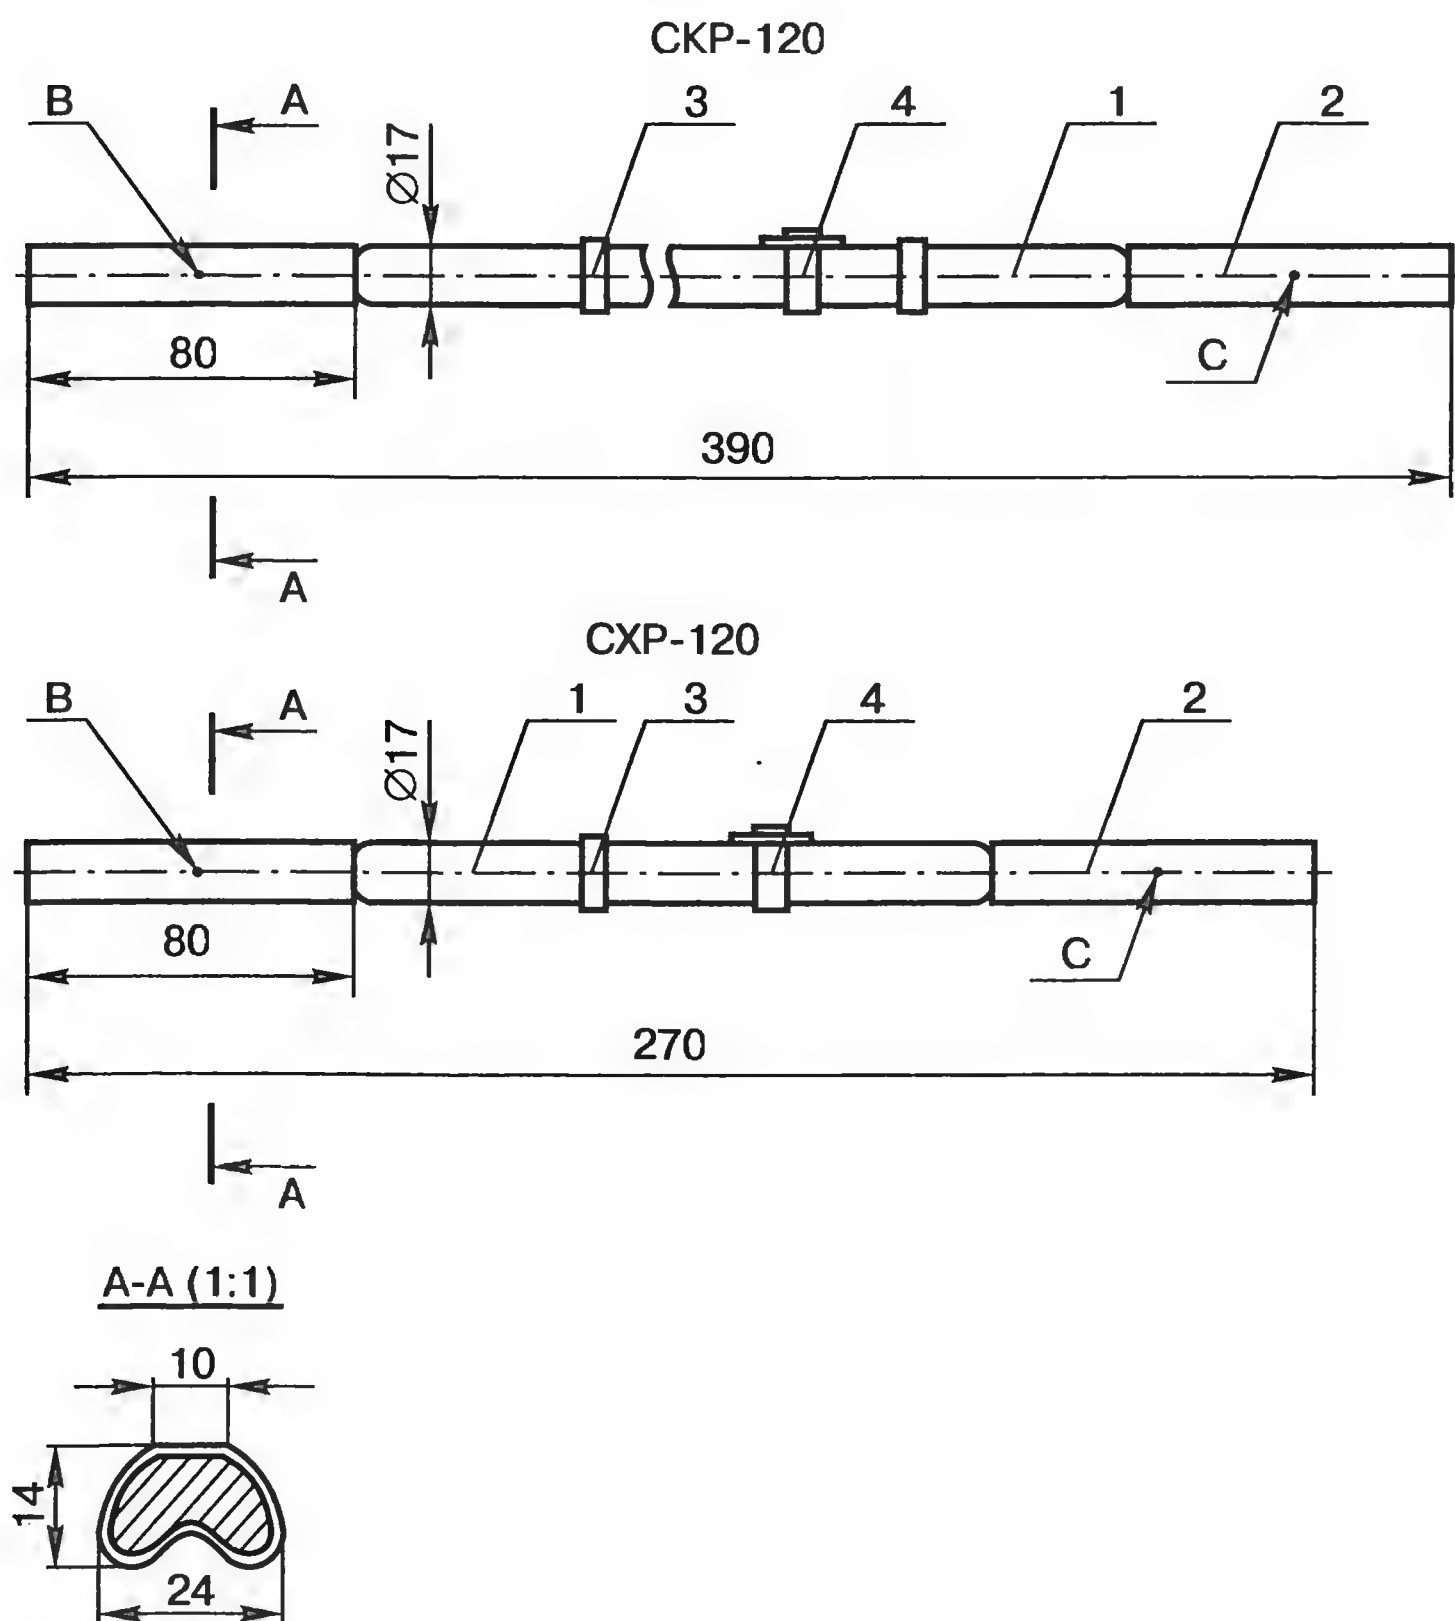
Соединители медные типов SKP-120 и CXP-120
